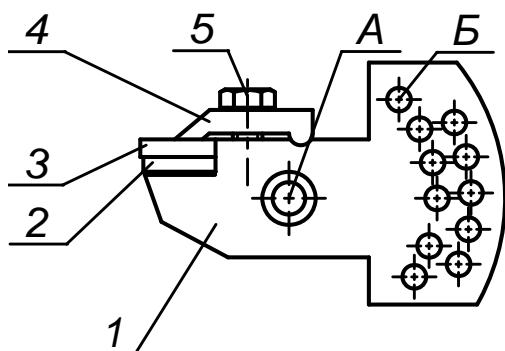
Нож с закреплением режущей пластины прихватом: 1 – державка; 2 – опорная плата; 3 – режущая плата; 4 – прихват; 5 – болт; А – осевое отверстие; Б – отверстия под фиксирующий болт
